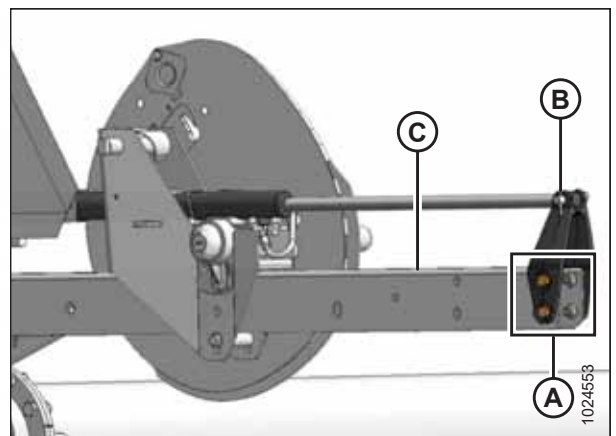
Циліндр правого важеля мотовила в передньому положенні
